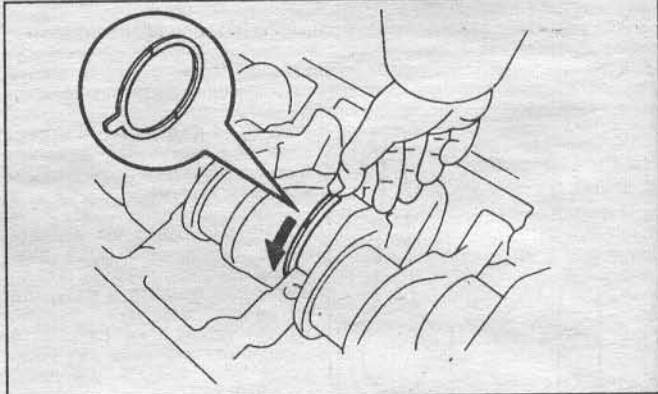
а Установите нижнее полукольцо осевого подшипника на центральную шейку вала масляными канавками наружу. Для облегчения установки их на место прокрутите вал.
